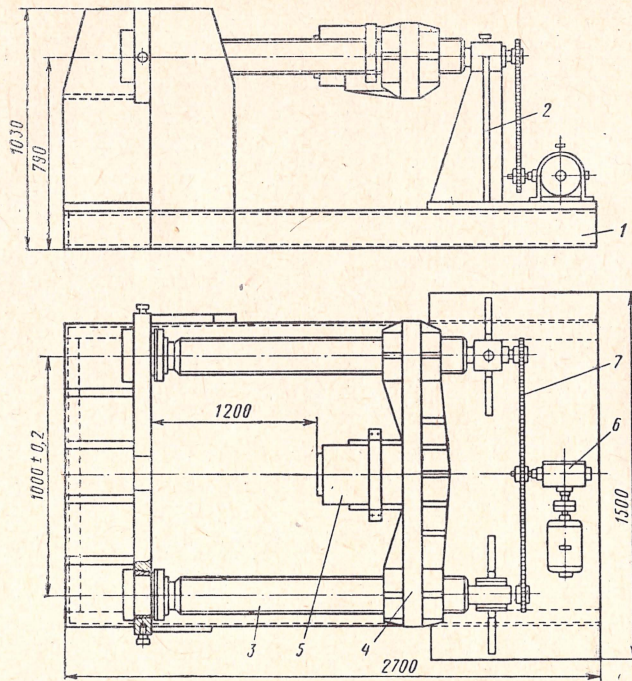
Горизонтальный гидравлический пресс для выпрессовки и запрессовки валов
